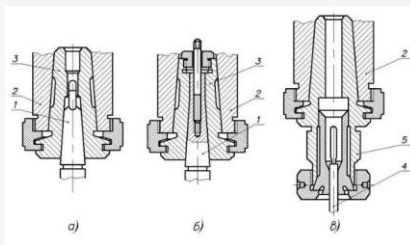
Установка інструменту на координатно-розточному верстаті
